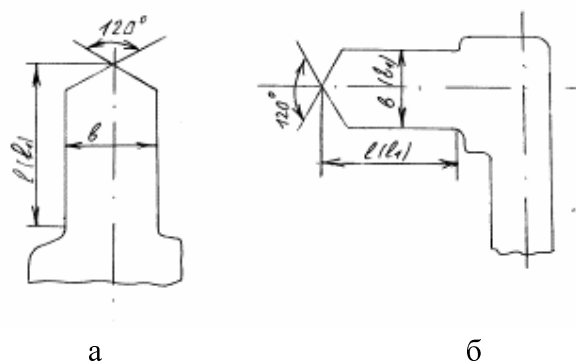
Загальна форма різців для виготовлення: а – болта; б – гайки.
